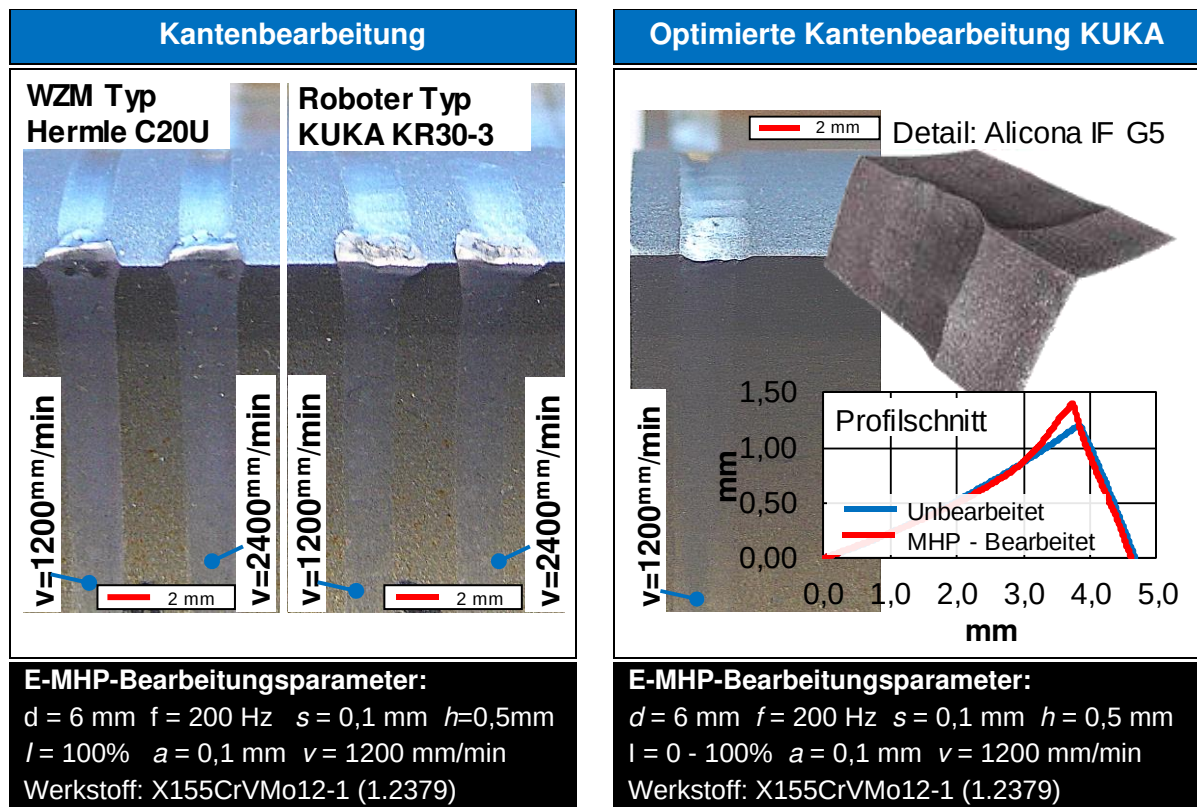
Optimierte Kantenbearbeitung mit dem E-MHP System, links: Gegenüberstellung der Kantenbearbeitung des sichelförmigen Bauteils aus Abbildung 33 durchgeführt am Roboter und der Werkzeugmaschine, rechts: gesteuerte Kantenbearbeitung des sichelförmigen Bauteils am Roboter
